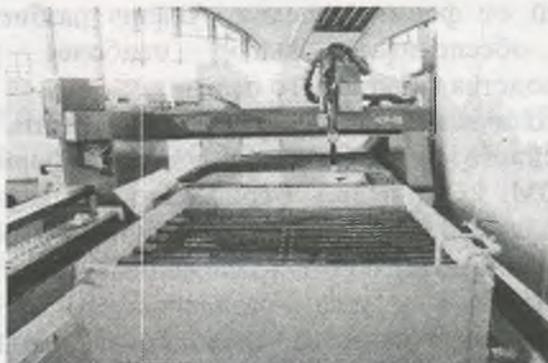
Автоматизированный комплекс плазменной резки КПр-02.
